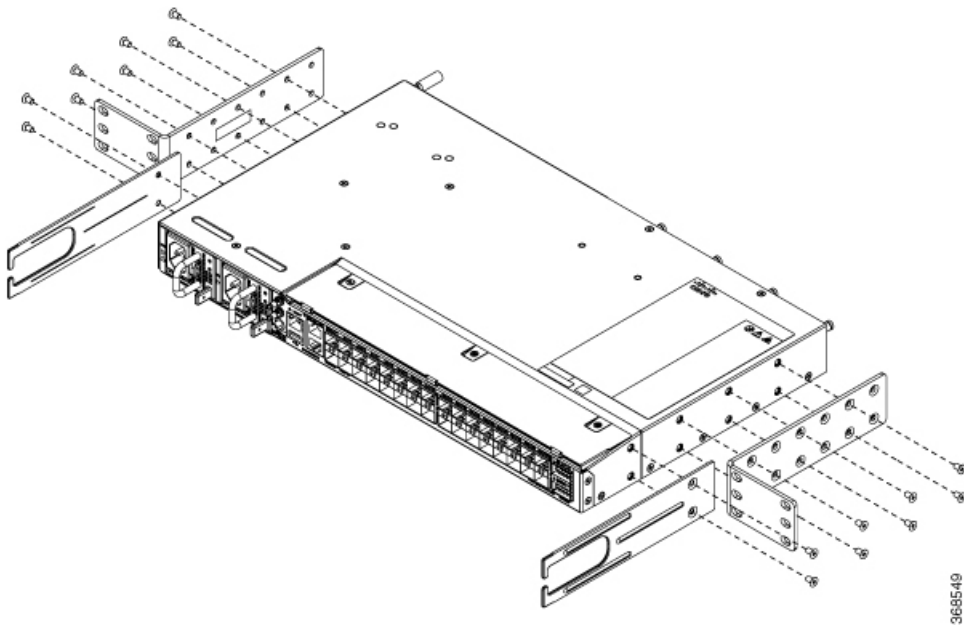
Instalación de los soportes de montaje en rack ETSI en la parte delantera
